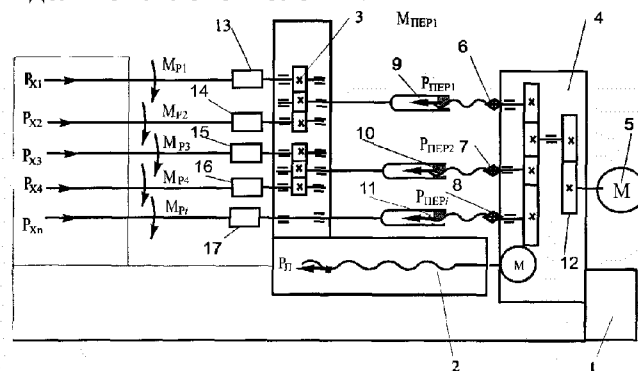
Силова багатошпindelна головка з механізмом керування пружними деформаціями із загальною ланкою настроювання
